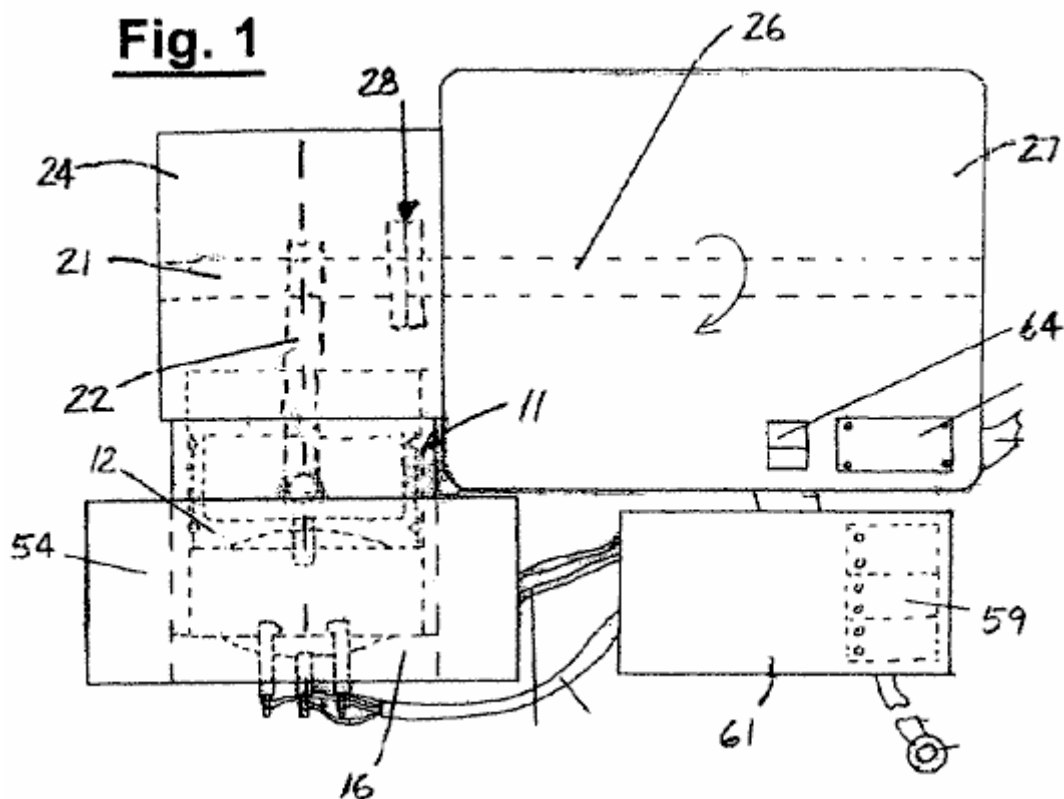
es una vista en planta superior de una realización de un motor de explosión interna y un generador que incorpora la invención.
